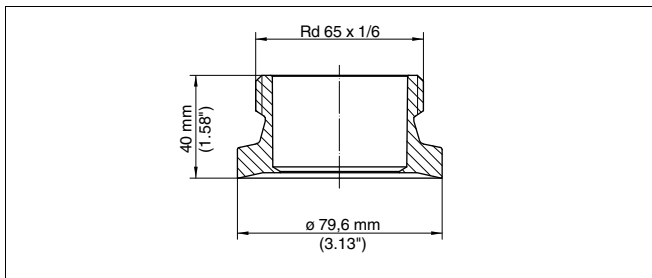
Medidas da luva soldada LA para porca de capa ranhurada
